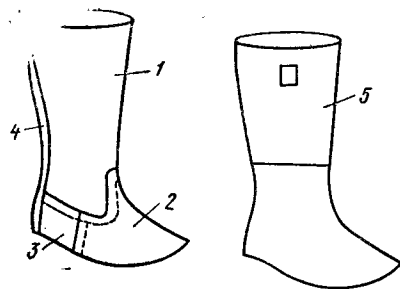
Детали верха сапог с голенищами из юфти:
